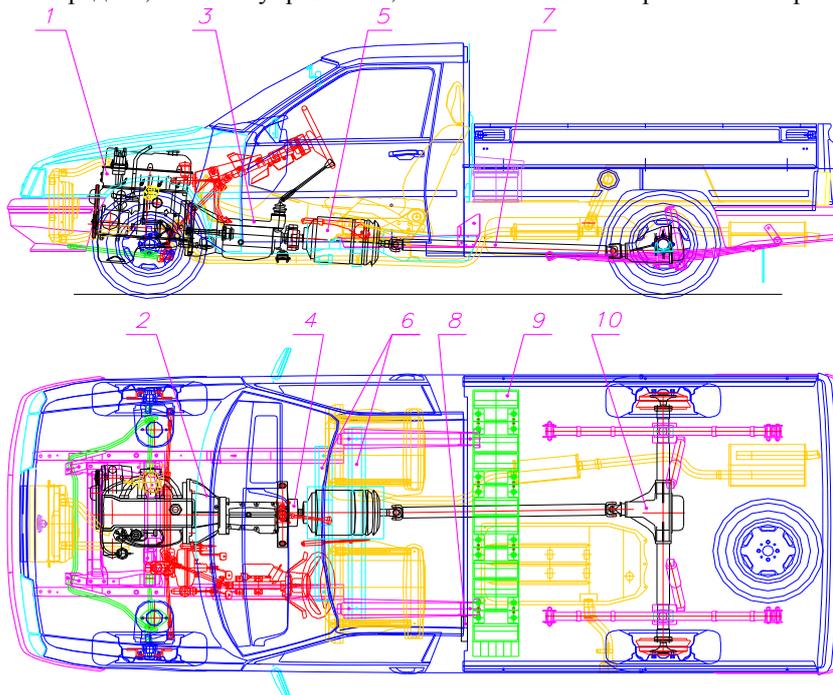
Общая компоновка гибридного автомобиля ИЖ-27171 (ДВС ВА3-2106 + ЭД ПТ-125-12): 1 – ДВС, 2 – сцепление, 3 – коробка передач, 4 – соединительная муфта, 5 – электродвигатель, 6 – опоры электродвигателя, 7 – карданная передача, 8 – блок управления, 9 – накопитель электрической энергии, 10 – задний мост
